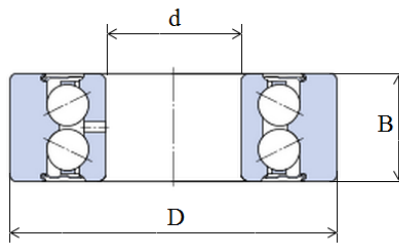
Principais dimensões para rolamento selecionado. Adaptado de [29].
